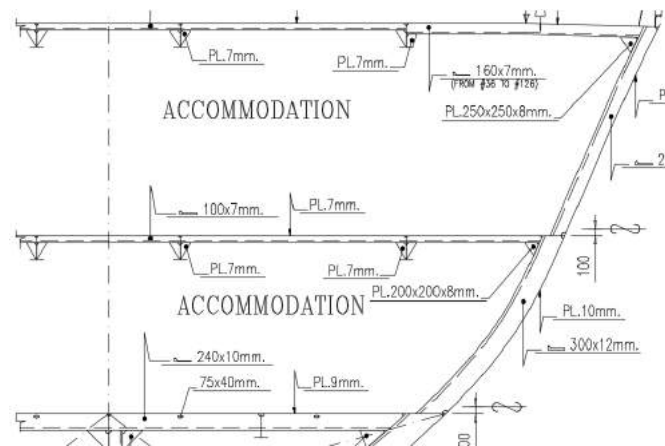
Estructura Transversal tipo. Fuente: SENER
